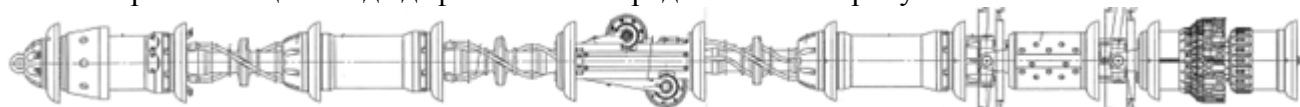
Чертеж общего вида дефектоскопа внутритрубного магнитного 6-МСК.00-00.000
